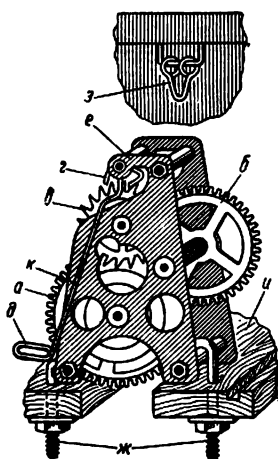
Механизм ходика: а — блочное колесо; б — промежуточное колесо; в — ходовое колесо; г — якорь; д — вилка; е — мост; ж — крючки крепления механизма к станку; з — качалка; и — станок; к — место сгибания вилки
